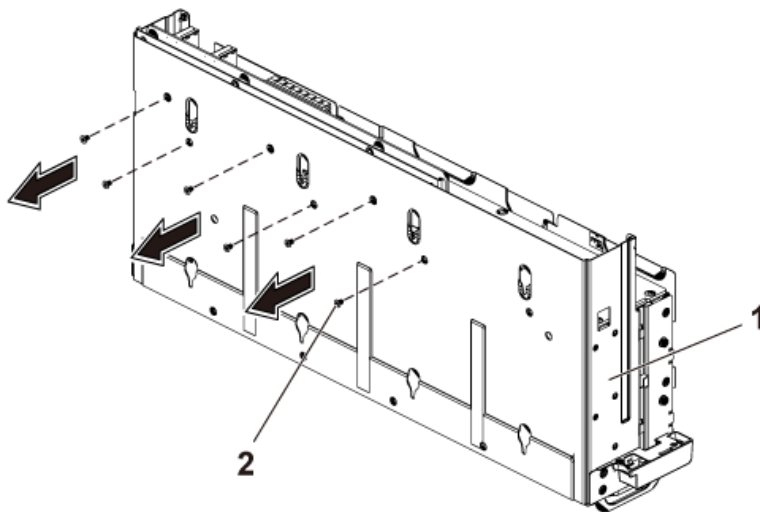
Entfernen und Einsetzen der Schrauben, mit denen die Erweiterungskartenbaugruppe am Laufwerkgehäuse befestigt ist
